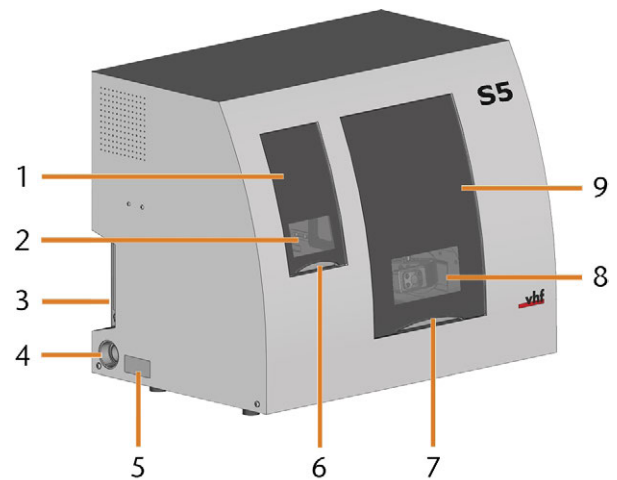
VISTA FRONTAL DE LA MÁQUINA
